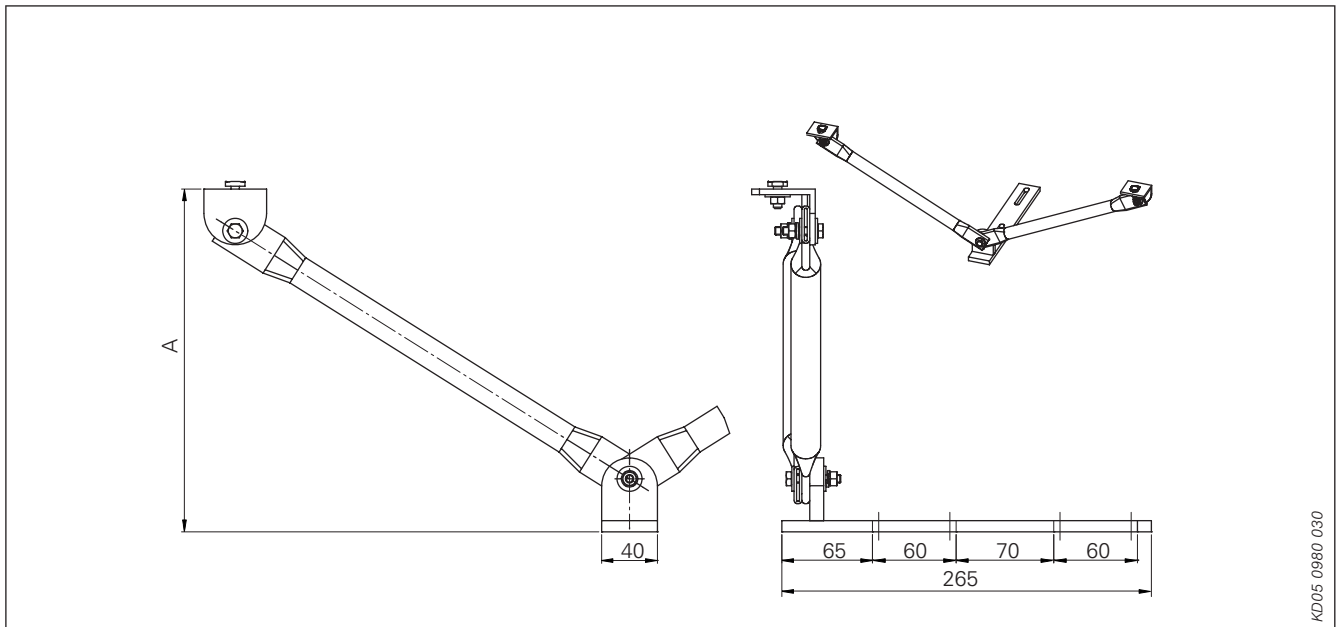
Soporte del carril guía nº 39 (soldado)
